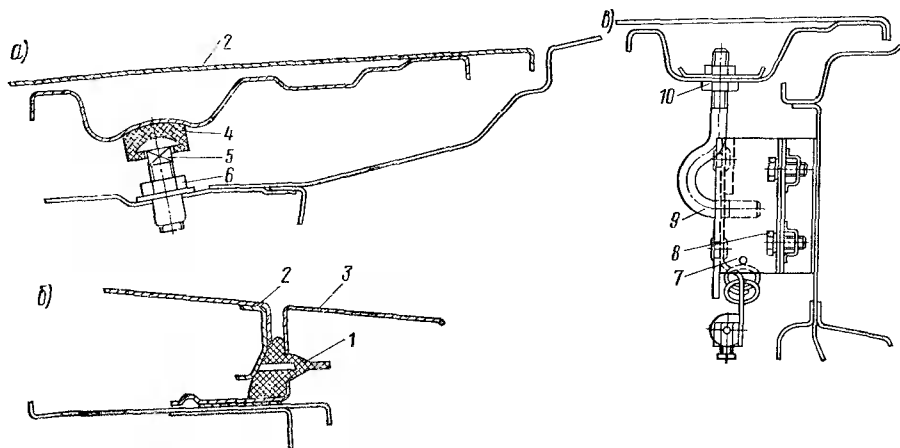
Регулировка крепления капота автомобиля «Москвич-408»: а — задний буфер капота; б — боковой буфер капота; в — замок капота
